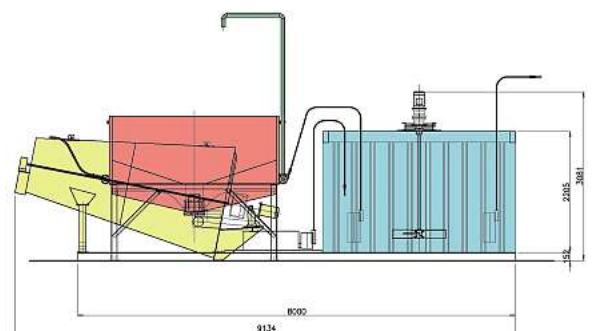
+ 6 Restbetonaufbereitung Typ BW10, Betriebsstellung
